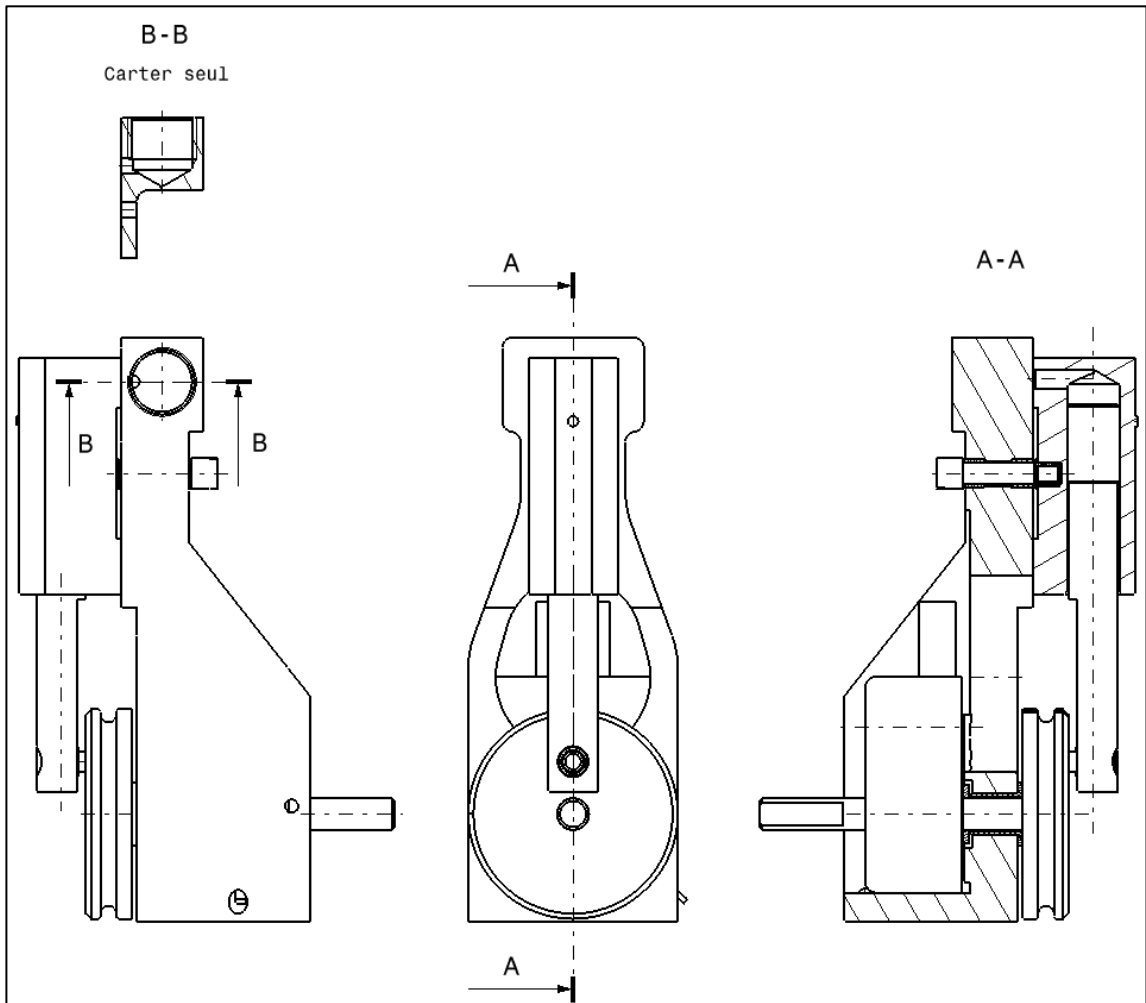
Extrait du dessin d'ensemble du moteur Ec de l'étude de cas « moteur à air »
